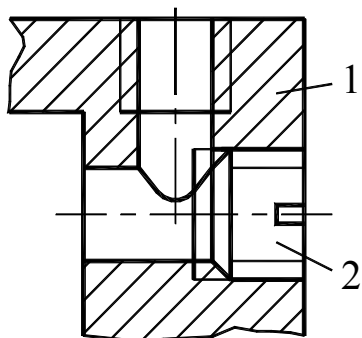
Склеивание резьбовой заглушки с корпусом: 1 – корпус, 2 - заглушка
